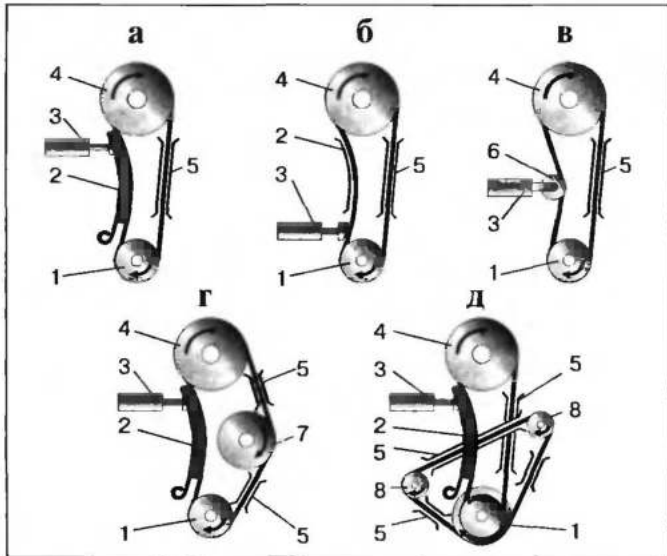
Схемы привода распределительного вала роликовой цепью:
